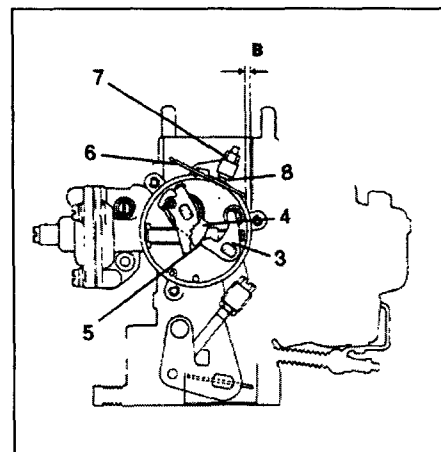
Регулировка пусковых оборотов - полуавтоматический привод
